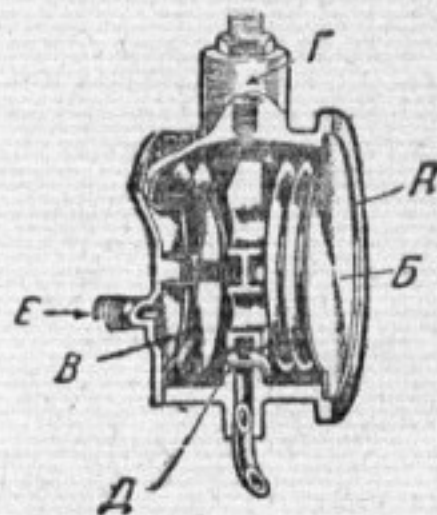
Автоматическая масленка для смазки стенок цилиндра и поршня
